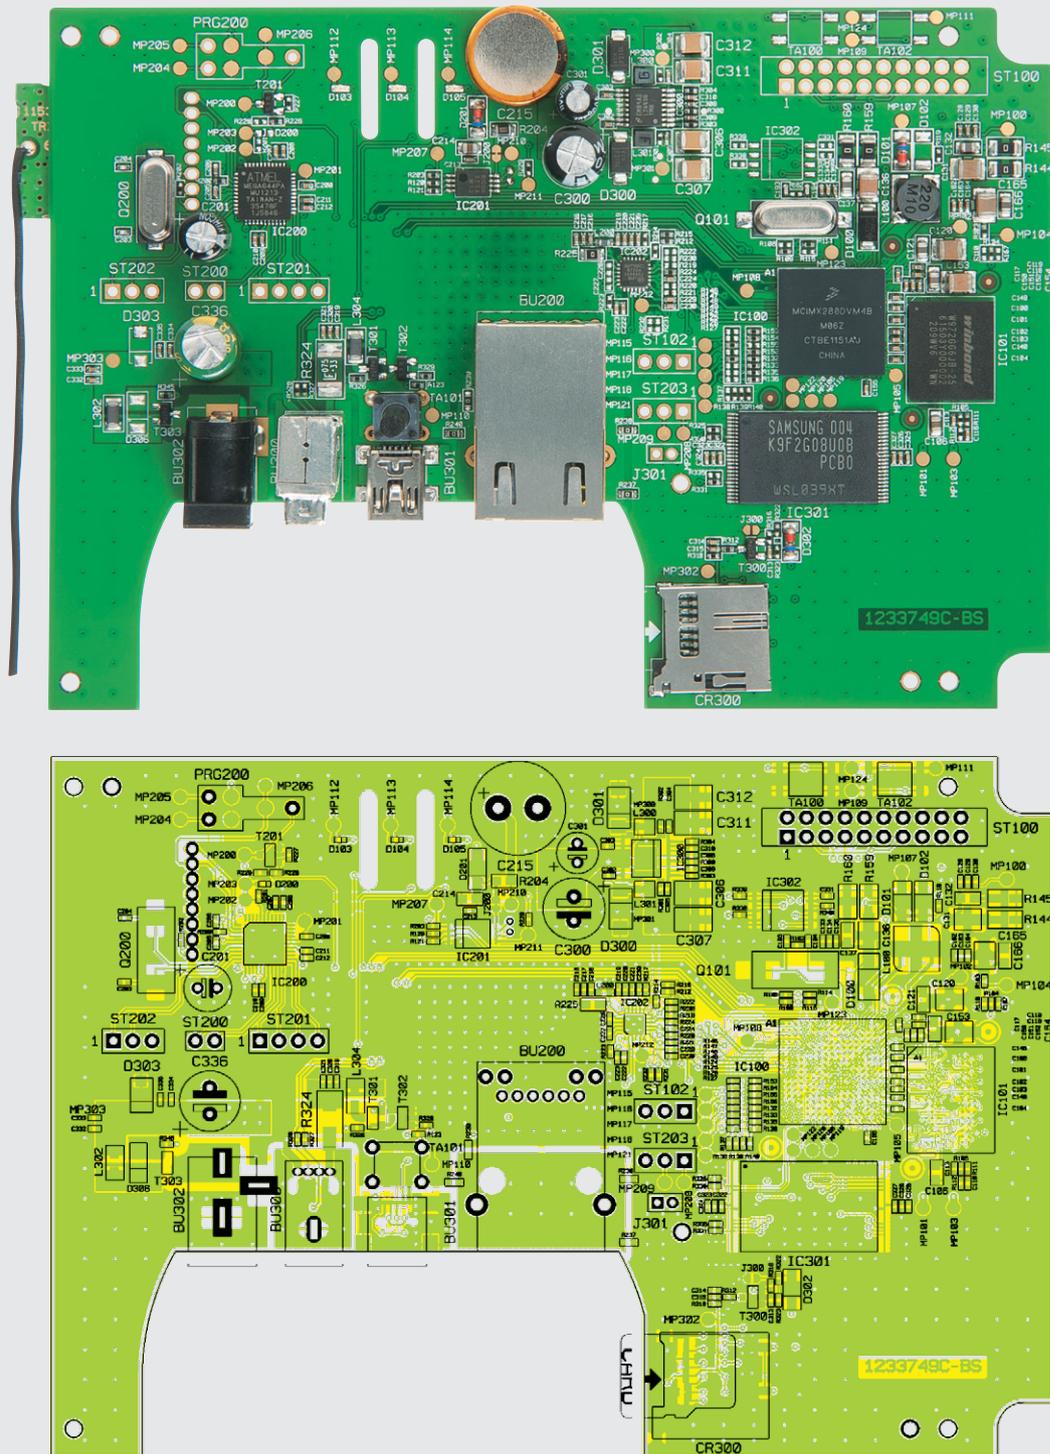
Platinfoto der komplett bestückten Platine (Oberseite) mit zugehörigem Bestückungsplan
